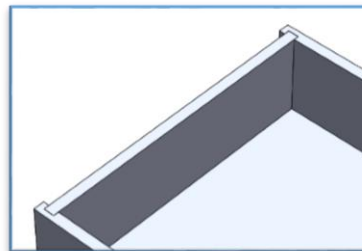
Detalle de mecanizado en madera Fuente: Dibujo propio
